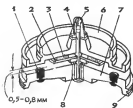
1. резиновые вкладыши; 2. пластмассовый фрикционный диск; 3. фетровая шайба; 4. ось узла; 5. пластмассовая заглушка; 6. подкассетник; 7. нижний диск; 8. втулка; 9. канавка для пассива.
